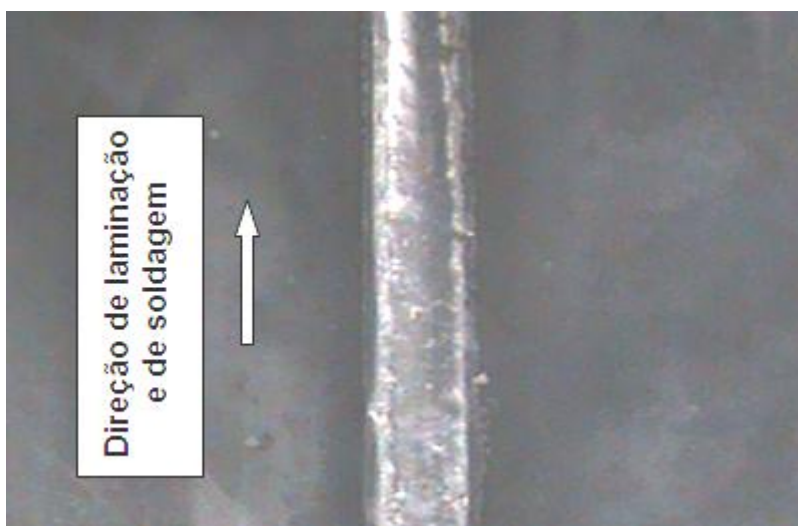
Fotografia das chapas soldadas mostrando a orientação da direção de laminação e do cordão de solda.
